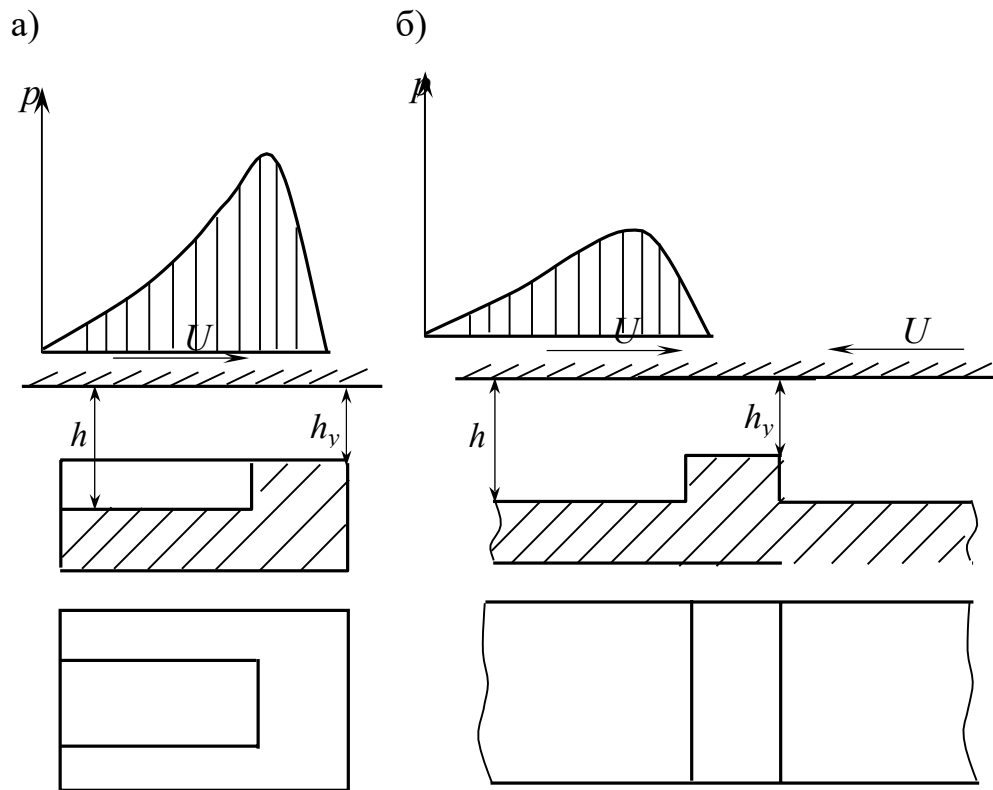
Схеми сегментів у формі сходинки Релея: а) із запірними кромками; б) реверсивний ПК
